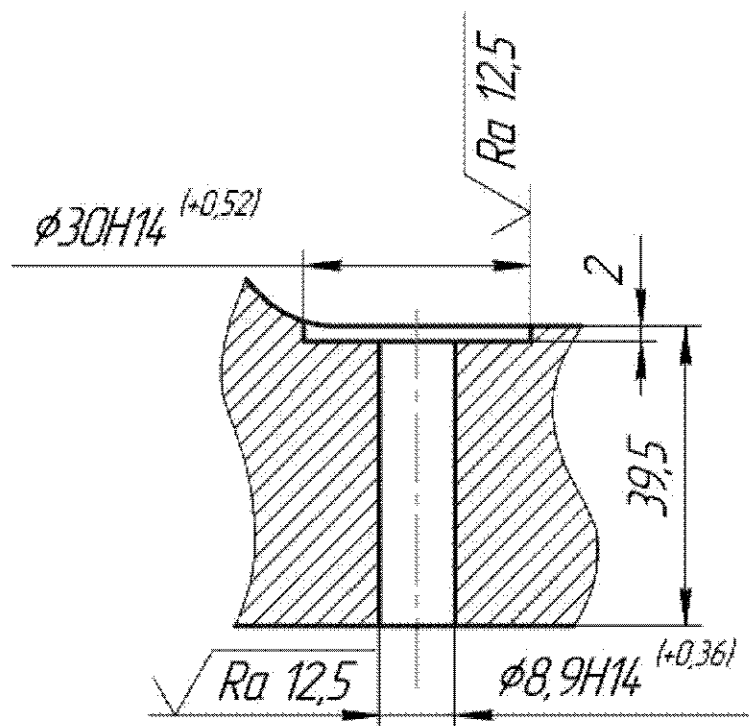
Эскиз обрабатываемой поверхности
